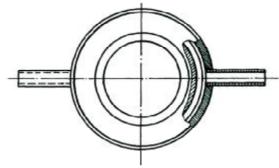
Спрейер щелевой в разрезе для закалки колонковых труб: 1 – корпус; 2 – регулятор; 3 – штуцер
